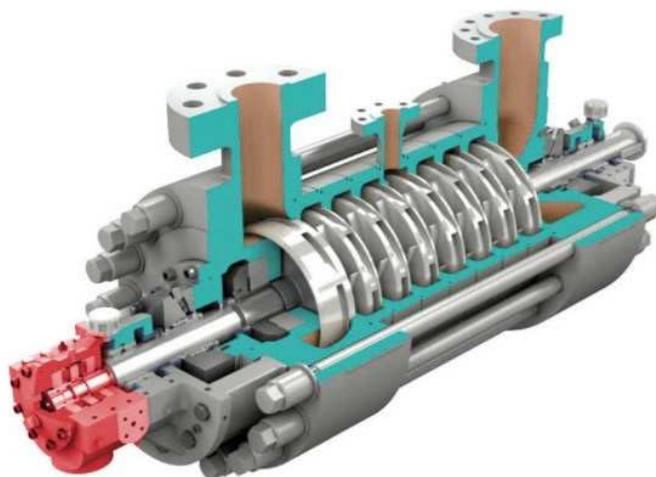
Многоступенчатый центробежный компрессор в разрезе
